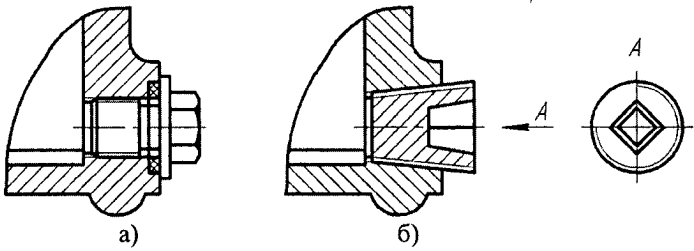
Зливний отвір з пробкою з циліндричною а) та конічною б)нарізками
